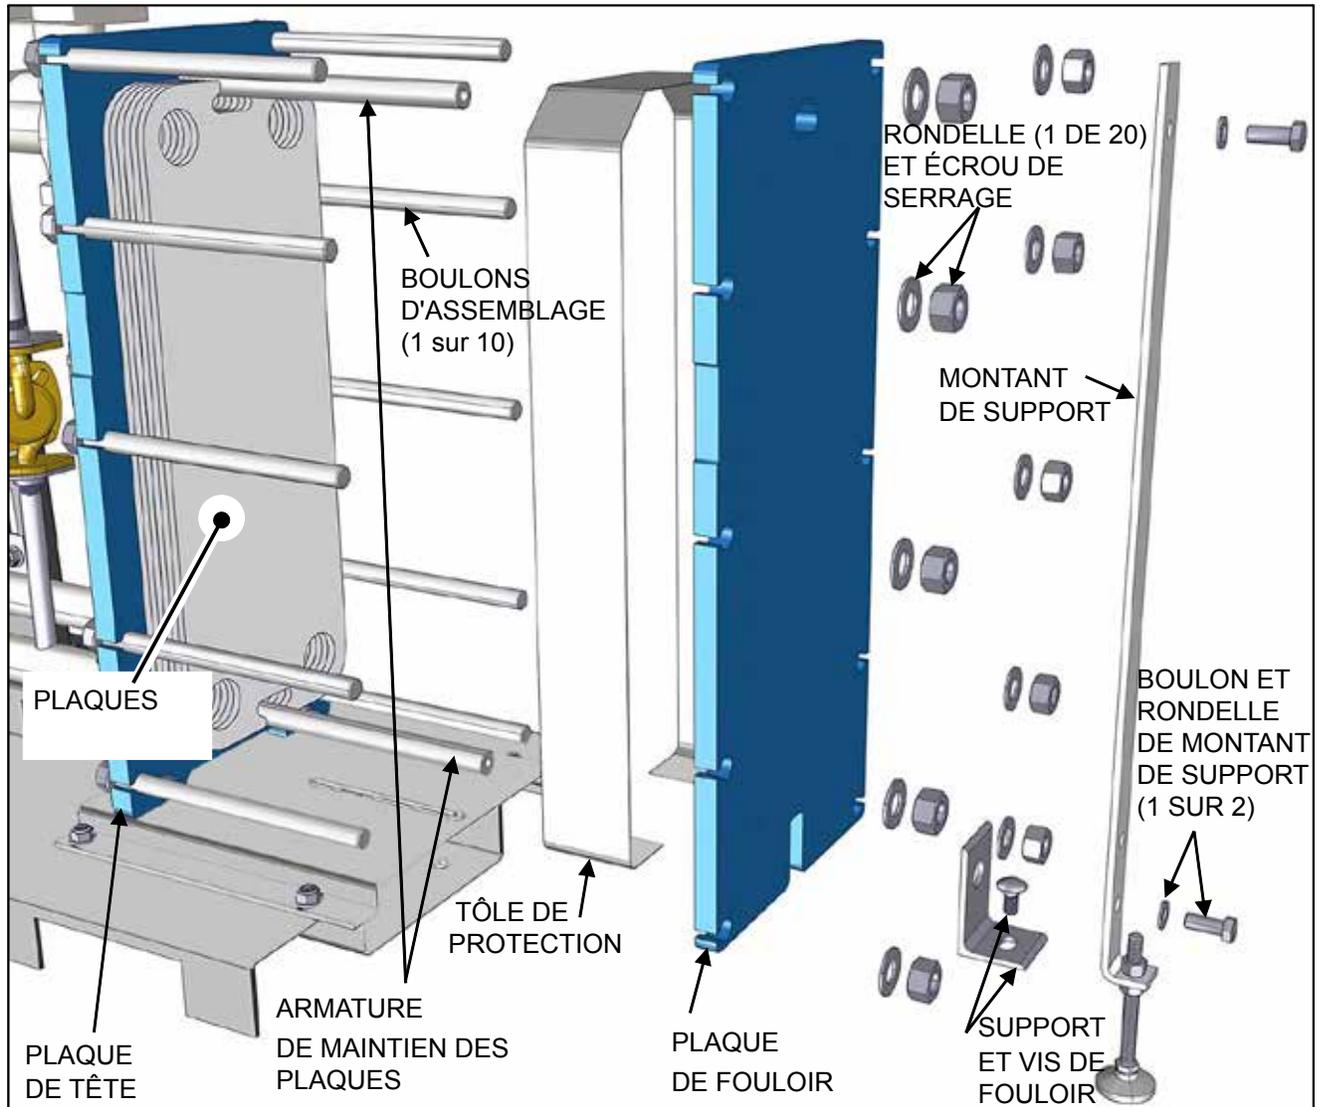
Pièces de l'échangeur thermique à plaques
